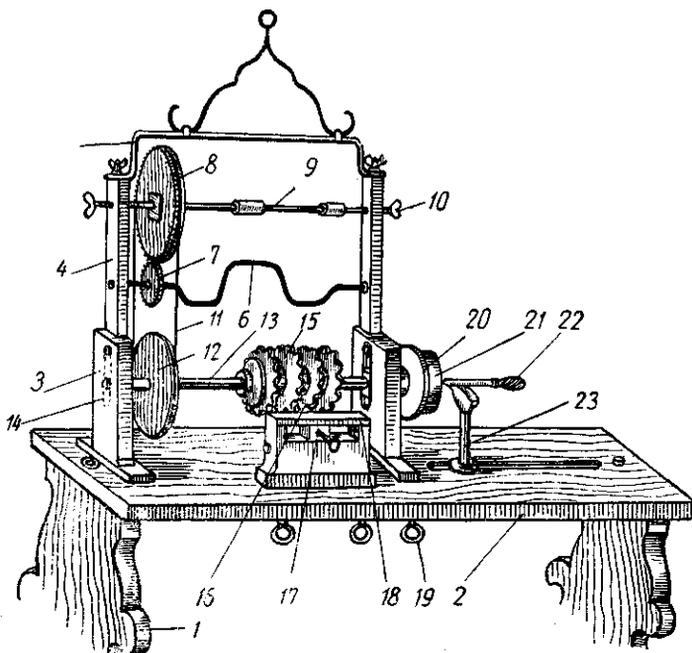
Кинематическая схема гильоширного токарно-овальерного станка Партова 1718 г.
